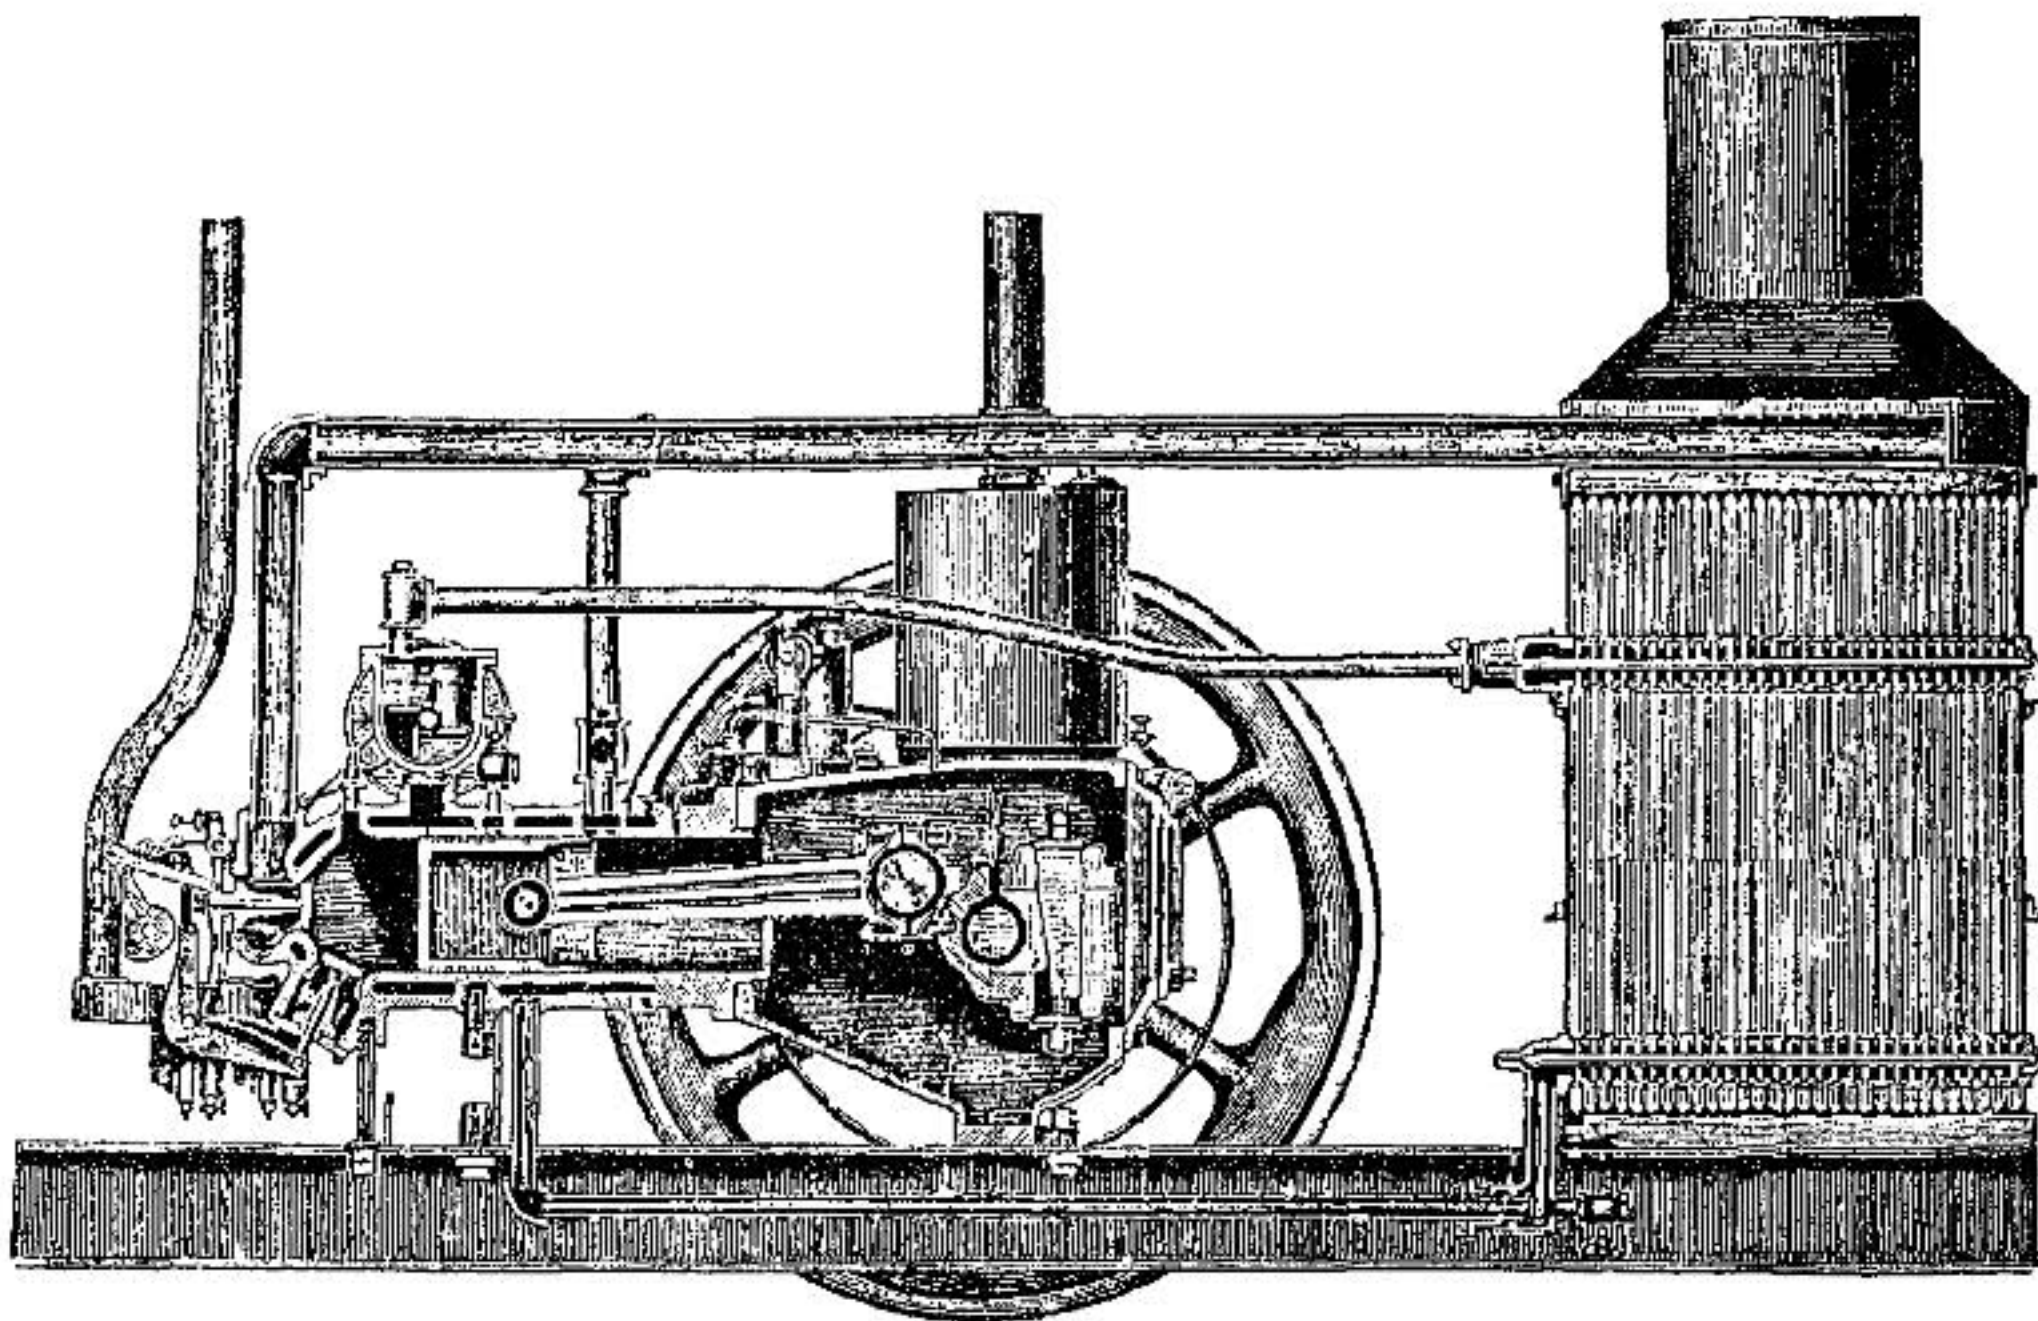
Схематическій разрѣзъ двигателя Гартъ-Паррѣ.
